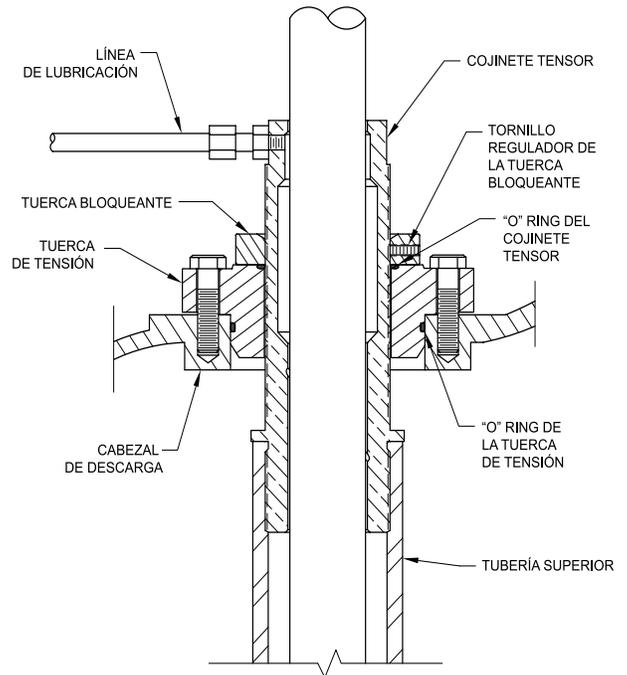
Conjunto Adaptador de Tubería Unidad Tipo "N260" y "Hi-Pro"
